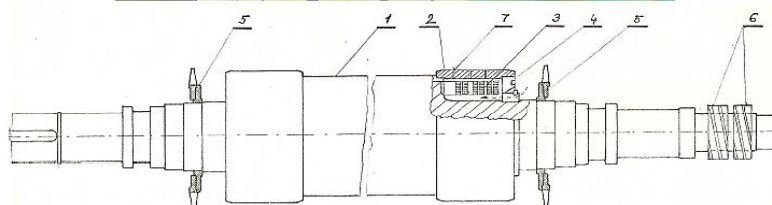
Synchronní stroj s hladkým rotorem [4]
